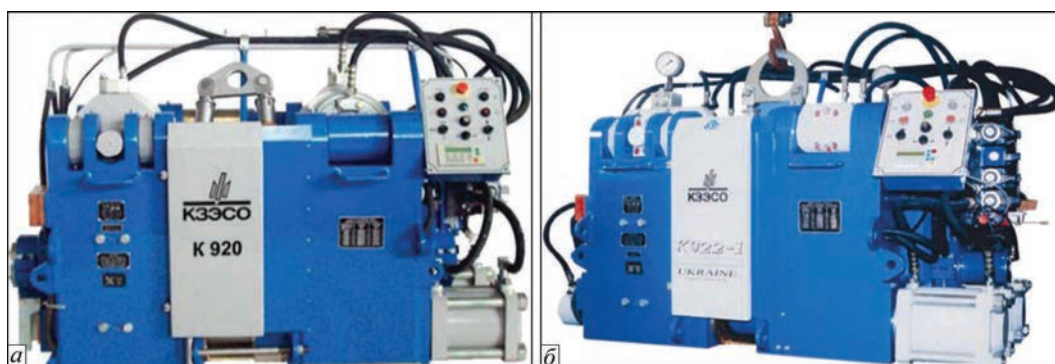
Мобильные машины для сварки рельсов: а — K920; б — K922-1
